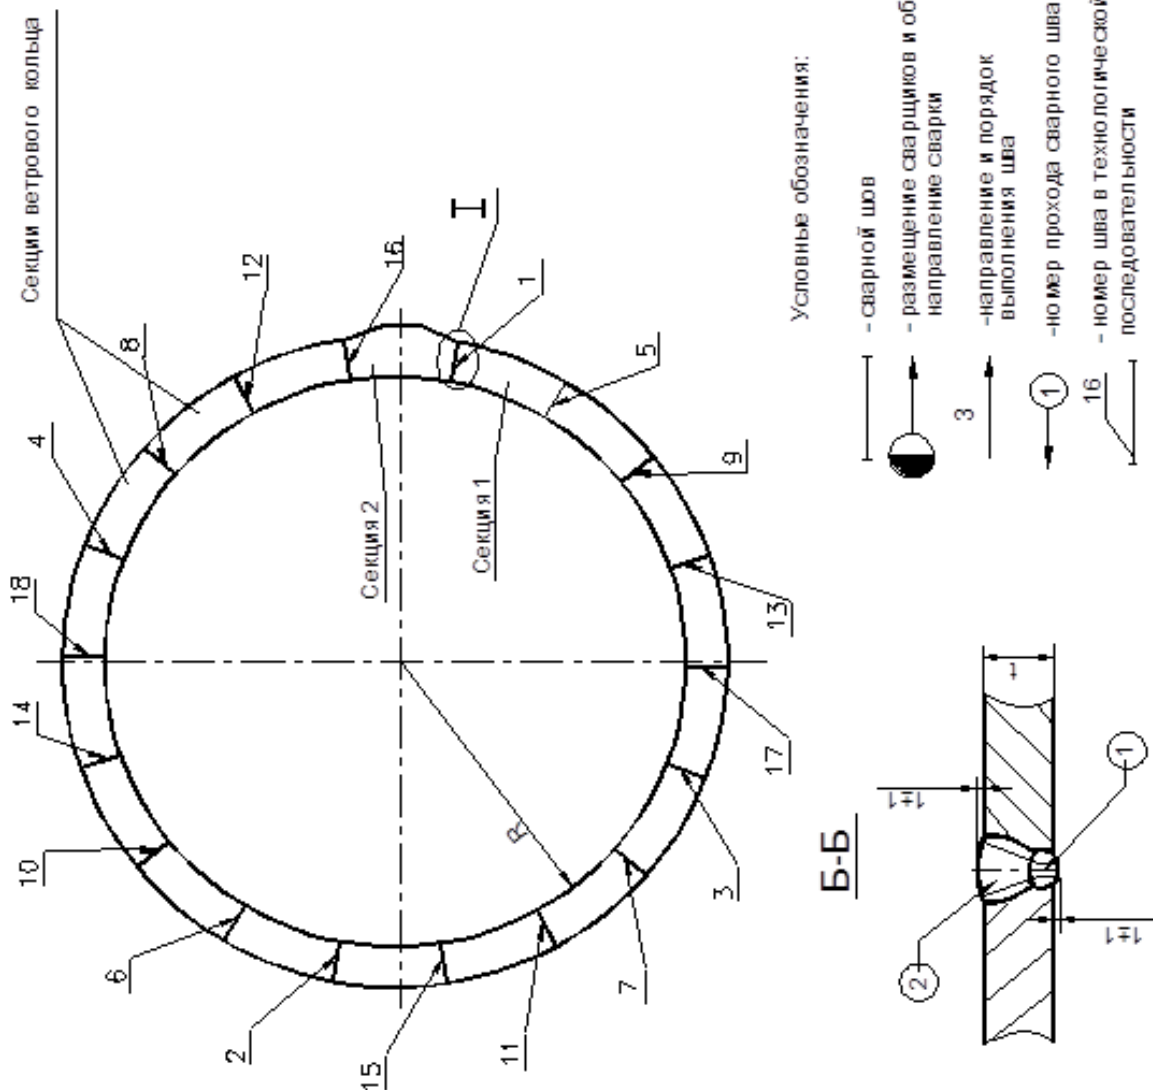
Последовательность сварки швов ветрового кольца
